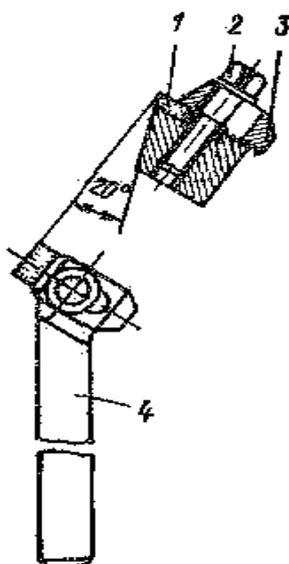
Резец с механическим креплением твердосплавных пластинок
